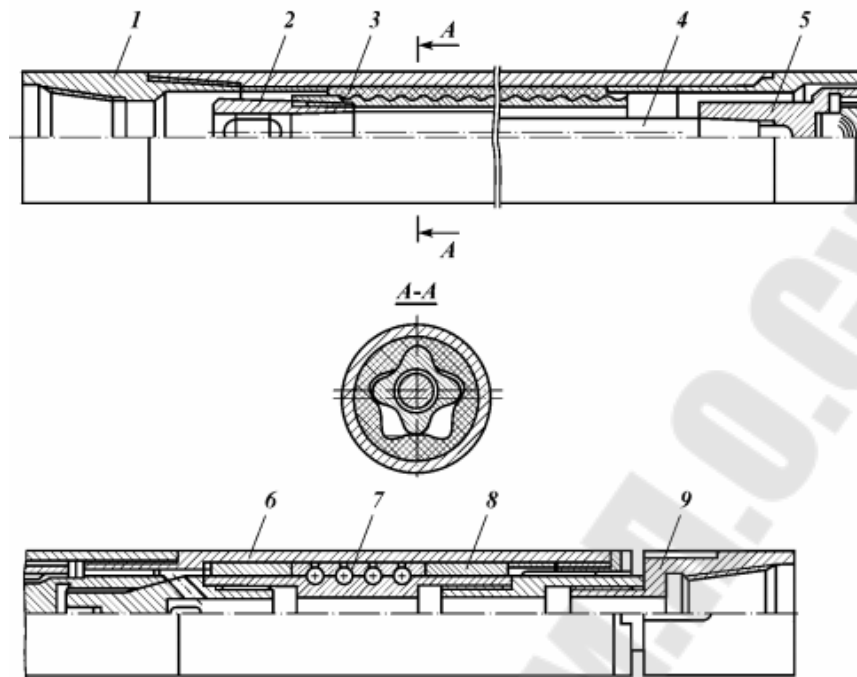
Винтовой двигатель ДГ-108 (укороченный, прямой) для горизонтального бурения: 1 – переводник верхний; 2 – ротор в сборе; 3 – статор; 4 – вал гибкий; 5 – шарнир; 6 – корпус шпинделя; 7 – опора осевая; 8 – опора радиальная; 9 – переводник наддолотный
